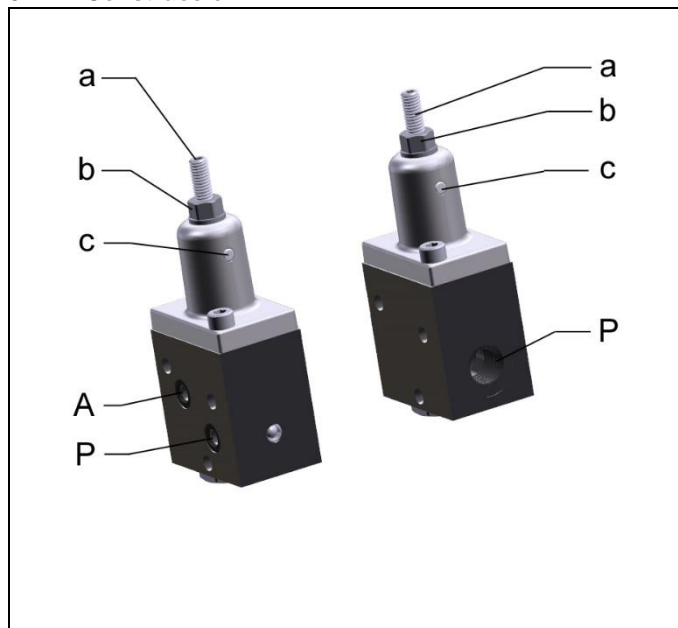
Posición de montaje de las válvulas (ilustración esquemática)
